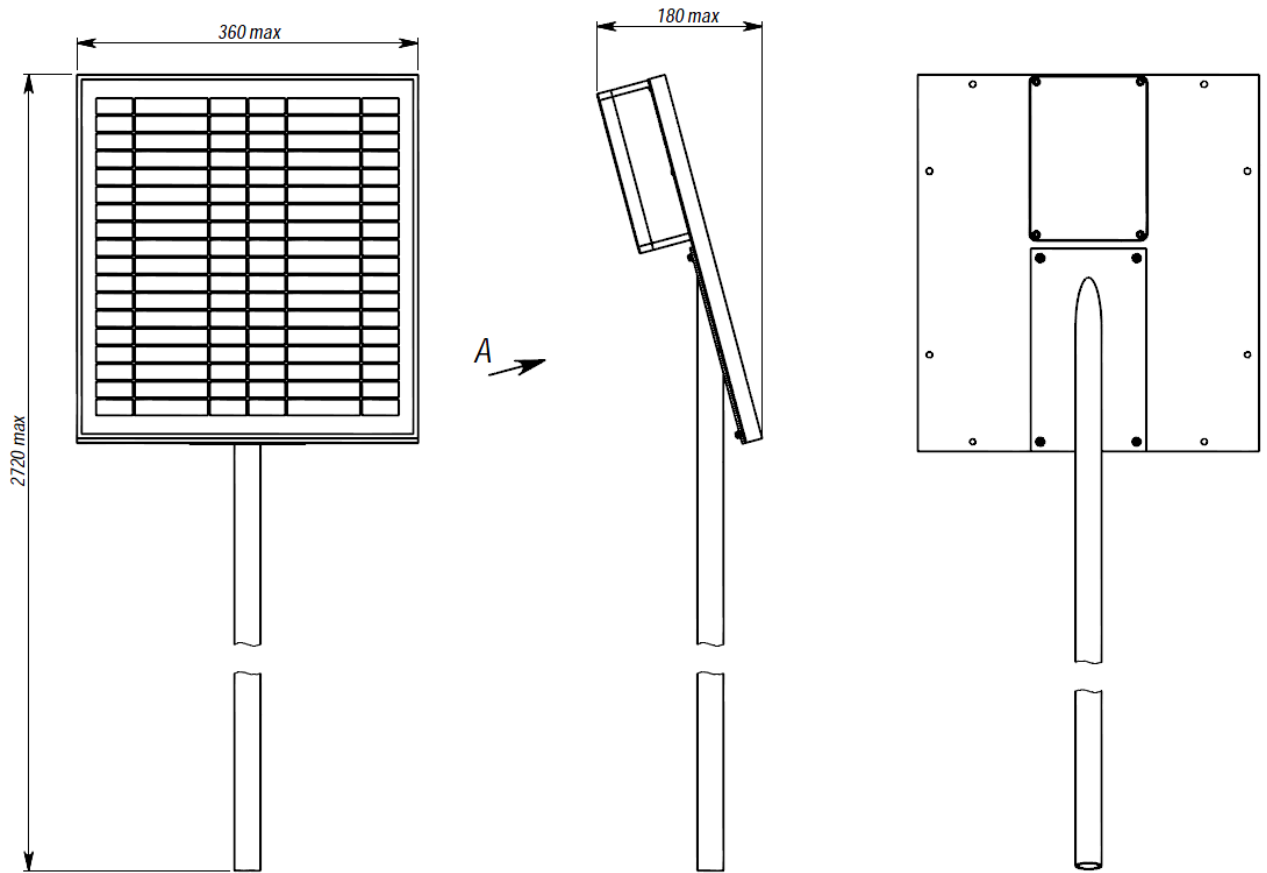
Вид и габаритные размеры сборки модуля Терминал с выносной стойкой
